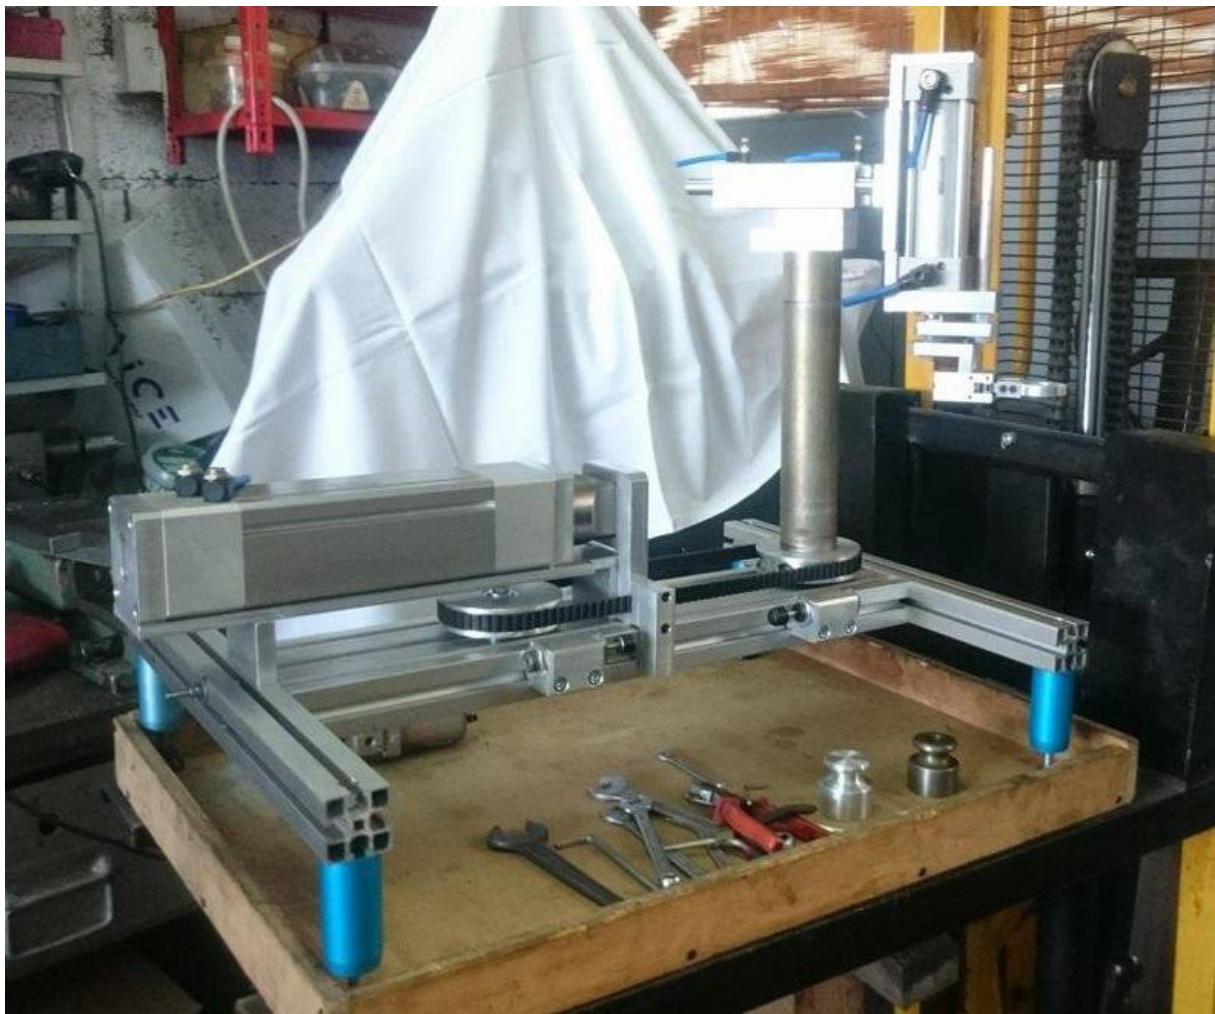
CNC stroj za izradu dijelova manipulatora
